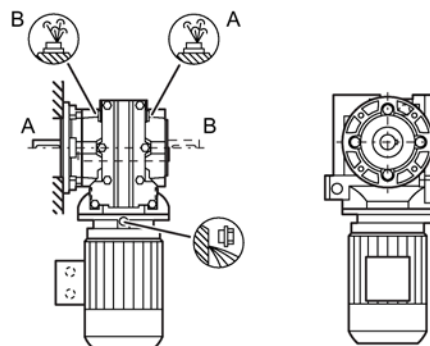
Монтажные положения для цилиндрического косозубого редуктора CAD в насадном исполнении, типоразмеры 39- 89
